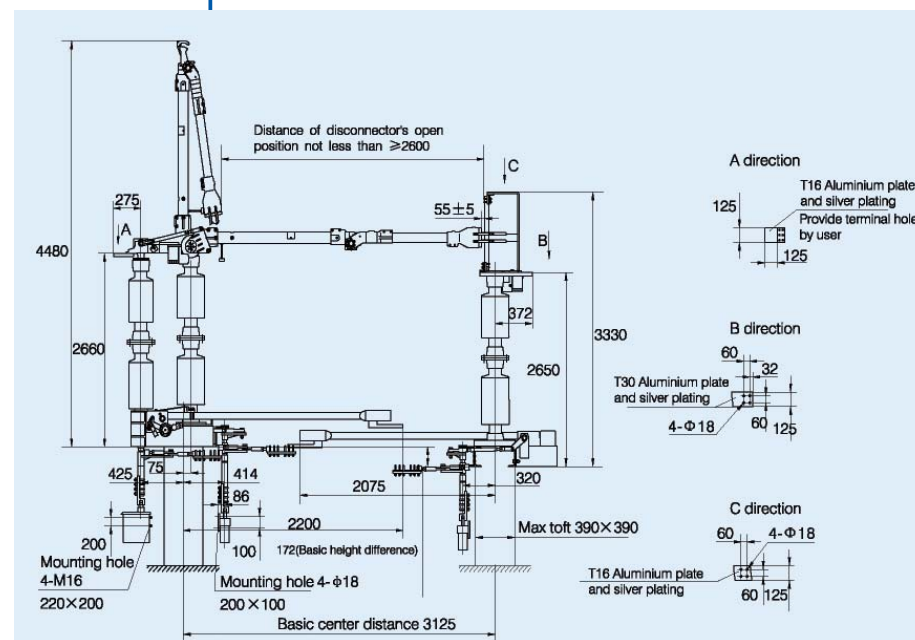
Внешний вид и размеры разъединителя GW23-252
